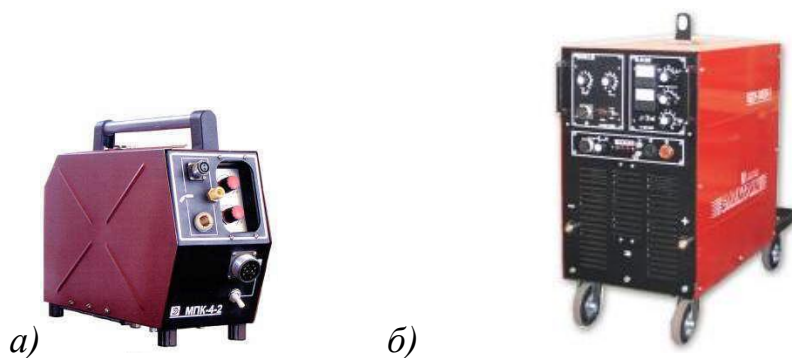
Применяемое сварочное оборудование: механизм подачи МПК-4-2 (а) и выпрямитель ВДУ-3020 (б)
